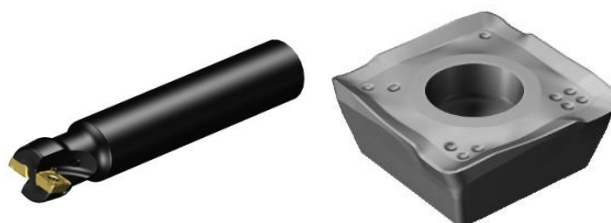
Fresa 490-020A20-08L / Inserto 490R-08T308E-ML H13A (Sandvik.com)
